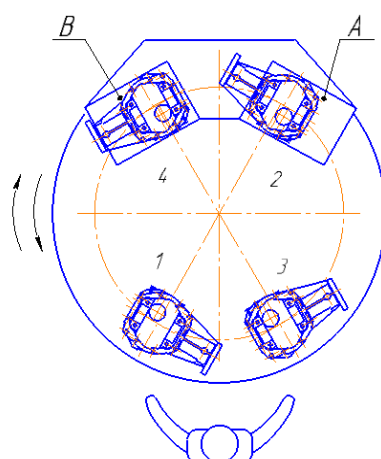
Сборочный установка с поворотным столом “Gehomat”
